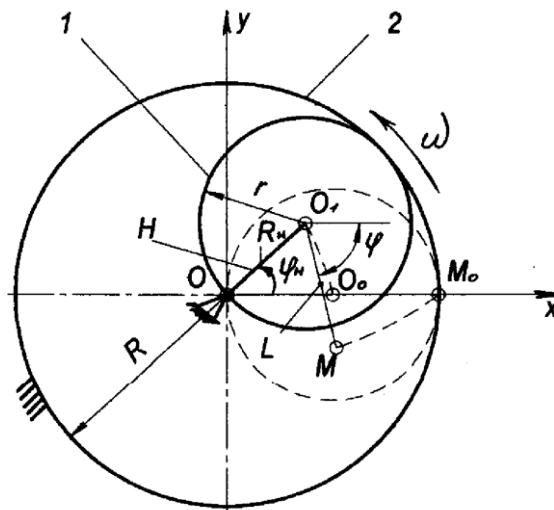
Розрахункова схема визначення параметрів планетарного механізму приводу ножа різального апарату:
